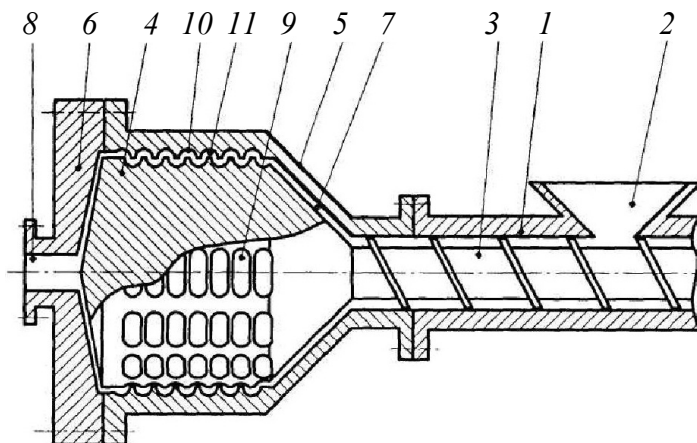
Конструкції дискового екструдера зі складеним обертовим диском (пат. України № 46781 U [47]): 1 – корпус; 2 – завантажувальний отвір; 3 – черв'як; 4 – диск; 5 – дискова частина корпуса; 6 – дискова кришка; 7 – дискова порожнина; 8 – розвантажувальний отвір; 9; 10 – заглиблення; 11 – хвилові канали
